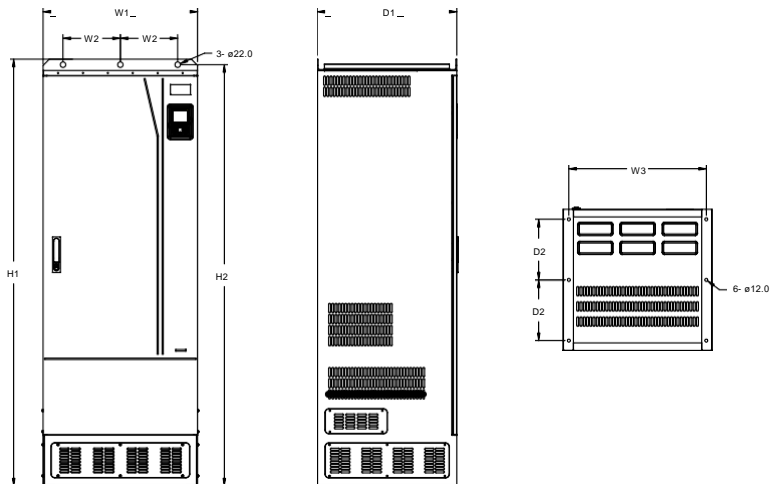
Схема для напольного монтажа ПЧ напряжением 660 В, от 400 до 630 кВт
